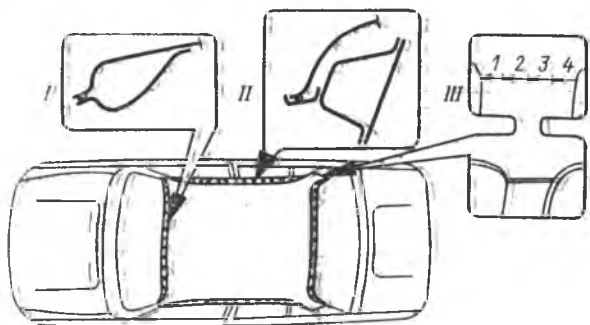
Сварка крыши с сопрягаемыми деталями:
